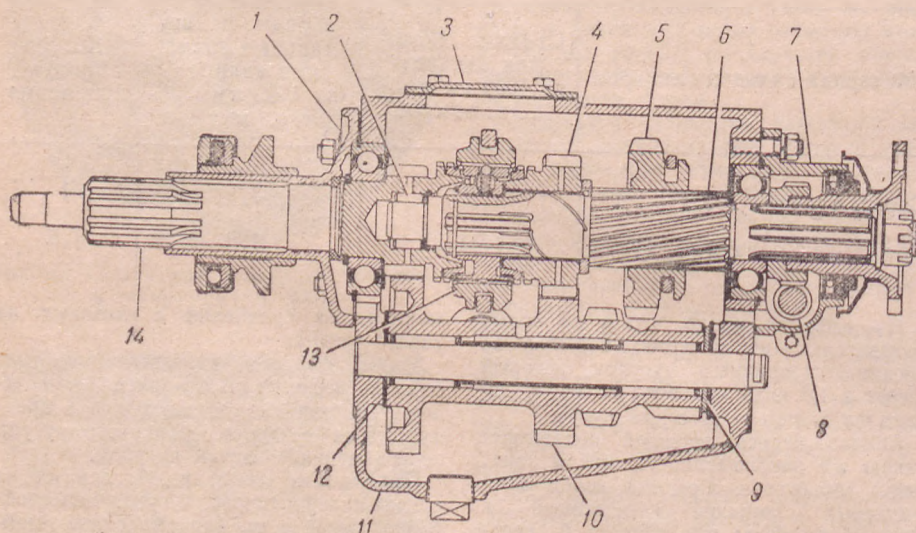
Новая коробка передач автомобиля М-20 „Победа“:
